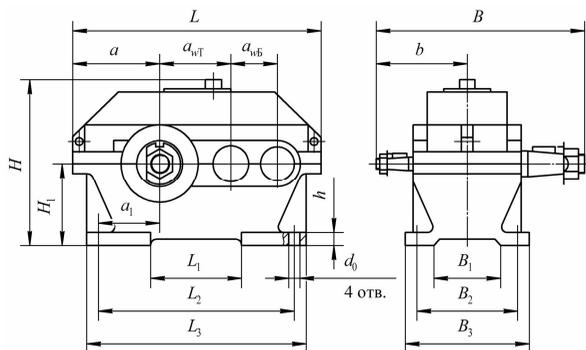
Основные габаритные, установочные и присоединительные размеры редуктора
